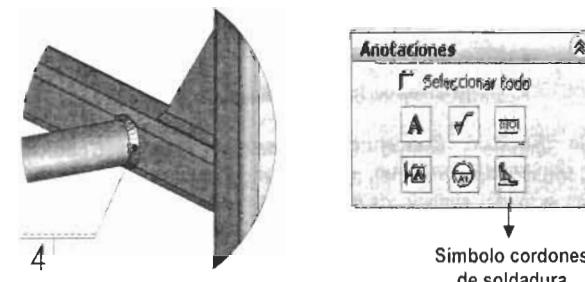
Inserción automática de Símbolo de soldadura.
